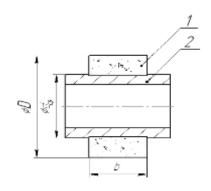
Эскиз заготовки торцевого алмазного круга формы 6А2
